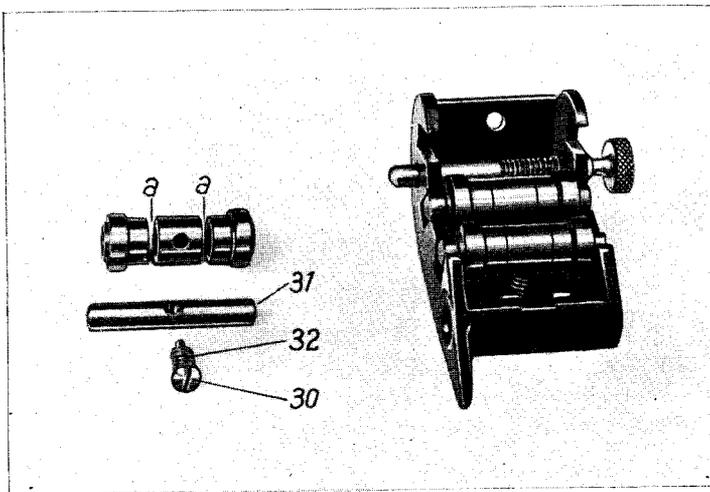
Rollenbahn mit ausgebauter Laufrolle
